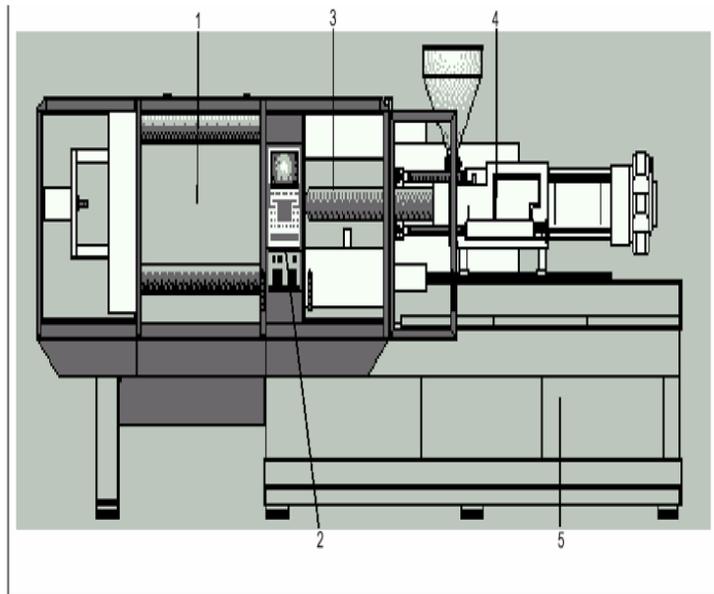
Descripción de las partes de la máquina de moldeo por inyección
